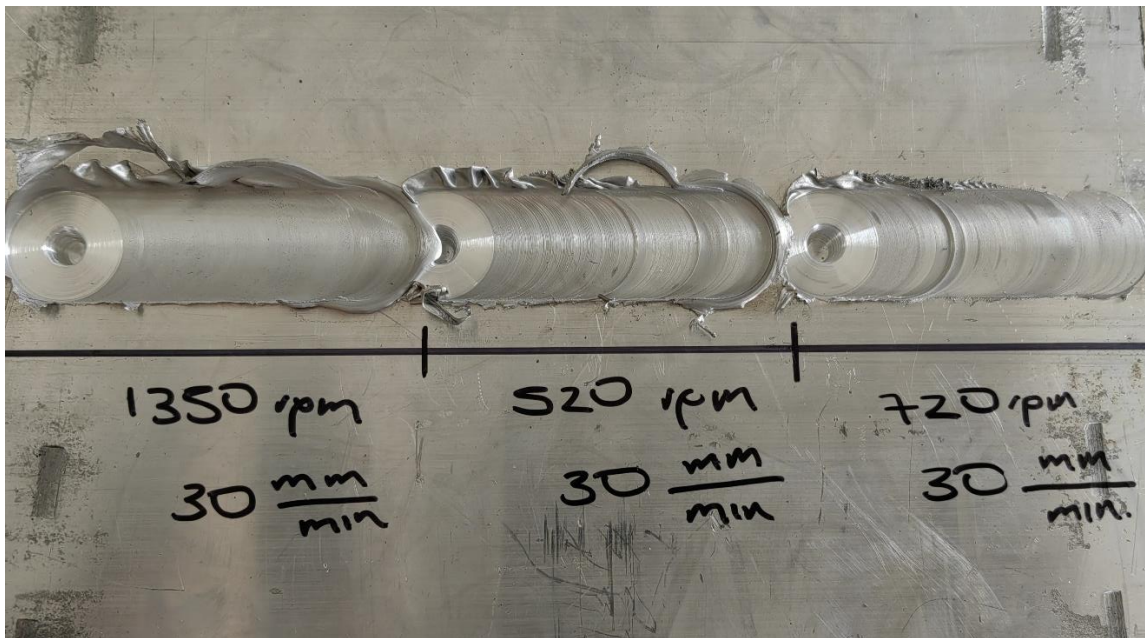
Adicionalmente, se observaron diferentes defectos de soldadura durante las pruebas, como la expulsión excesiva de material y túneles en la unión soldada.
